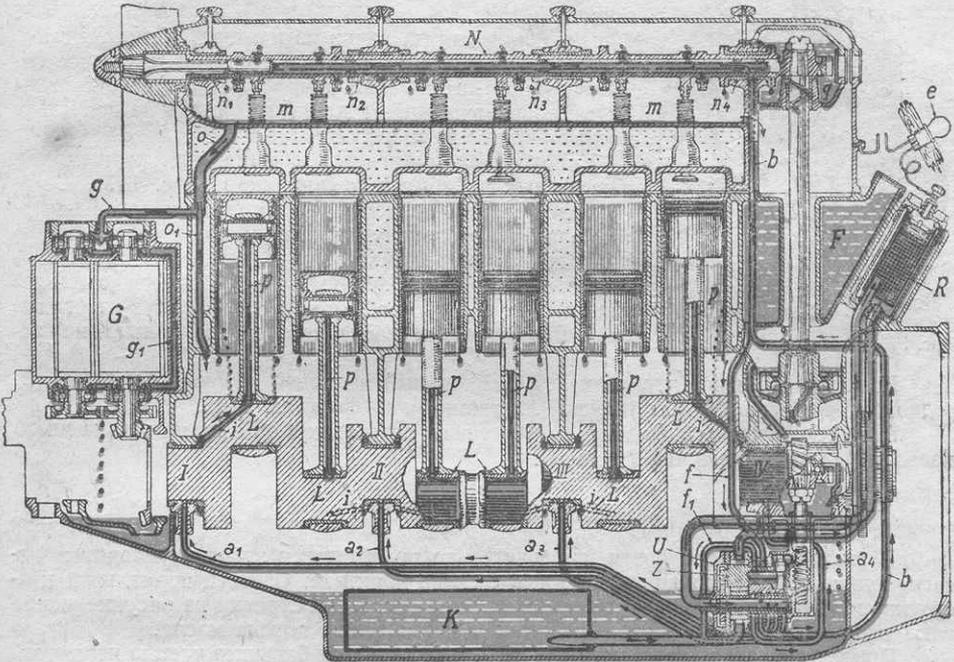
Схема смазки двигателя «Мерседес-Бенц» с компрессором.
